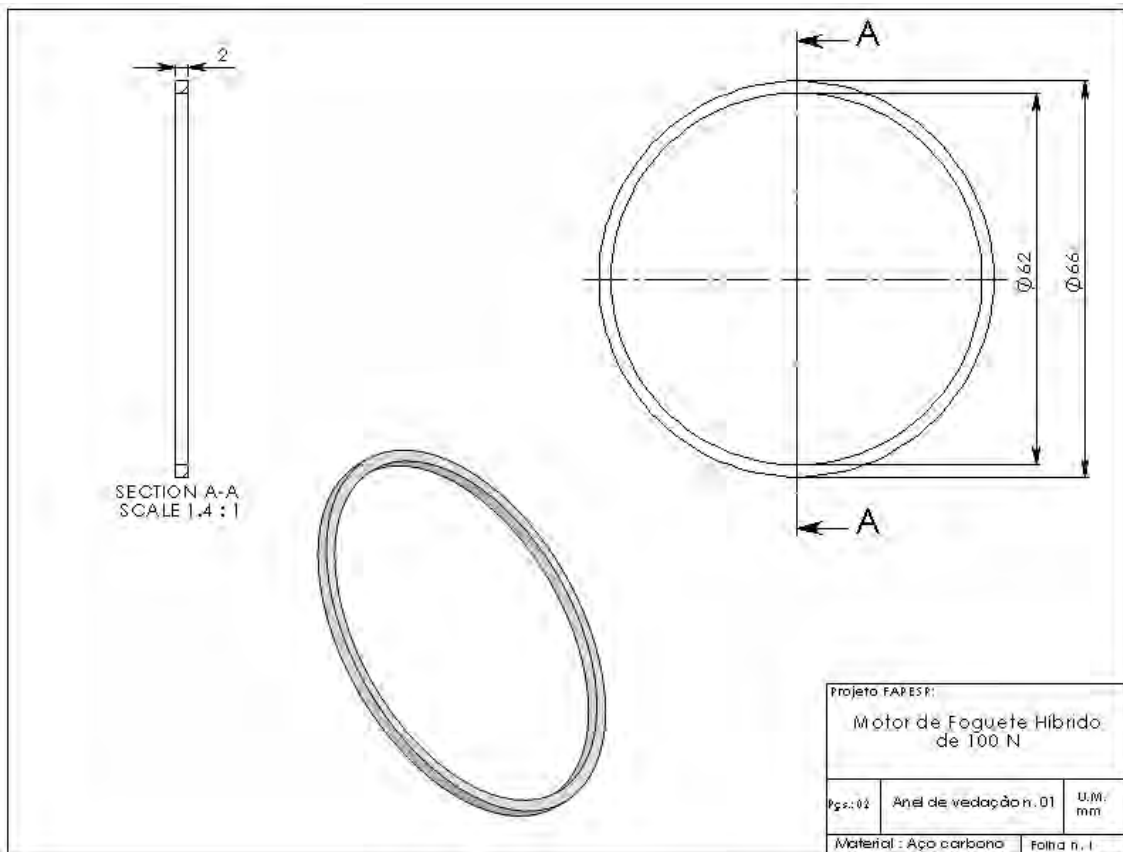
Desmontagem do motor foguete híbrido, cotas do anel de vedação do flange do injetor.
